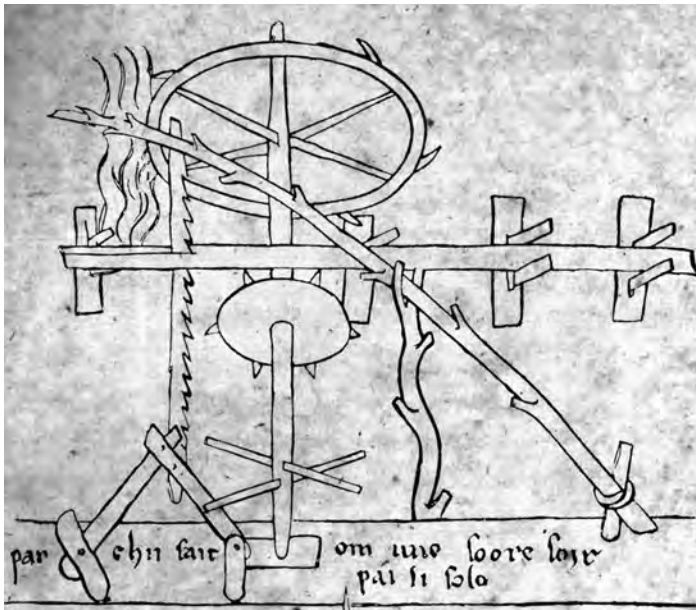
Skizze einer Sägemaschine von Villard de Honnecourt, ca. 1230.
